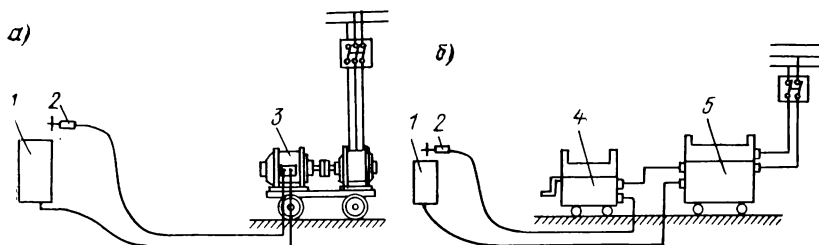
Схема сварочных постов: а — постоянного тока; б — переменного тока.
